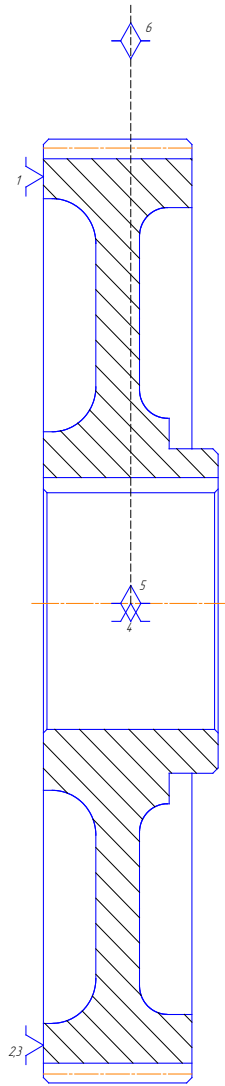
Теоретична схема базування для обробки поверхонь 1, 2, 3, 12
